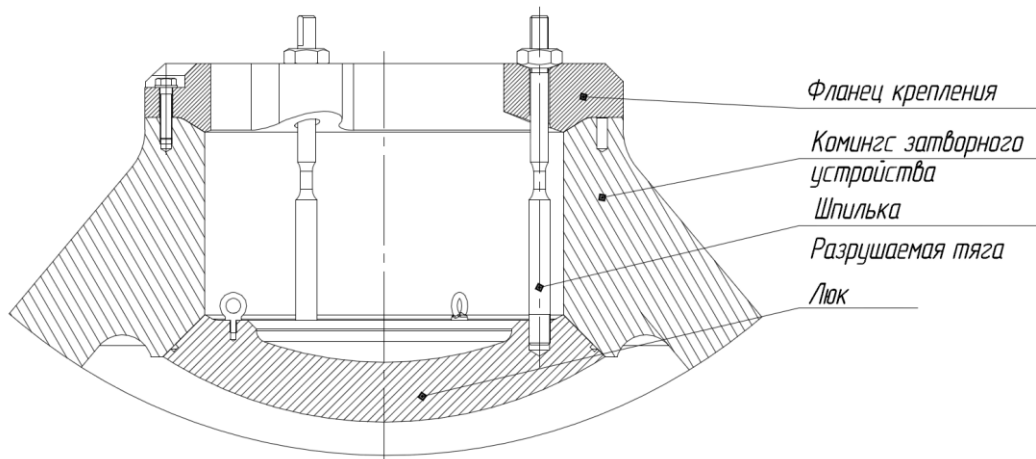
Принципиальный чертеж устройства аварийного сброса давления
